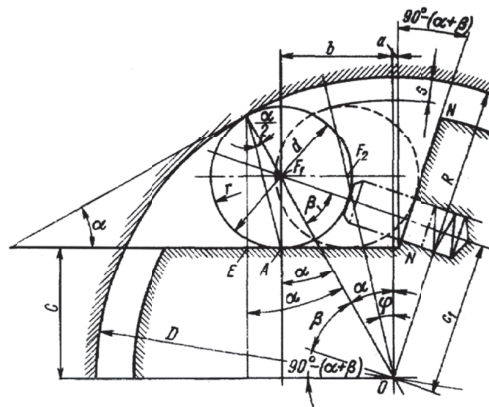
Муфта с цилиндрическими роликами и плоским профилем рабочей поверхности звездочки
